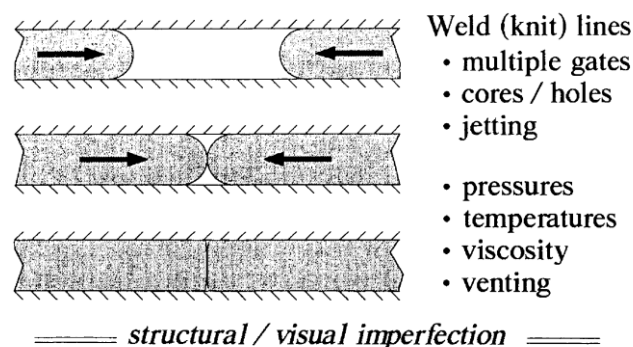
Linhas de soldadura. Adaptado de [19]
